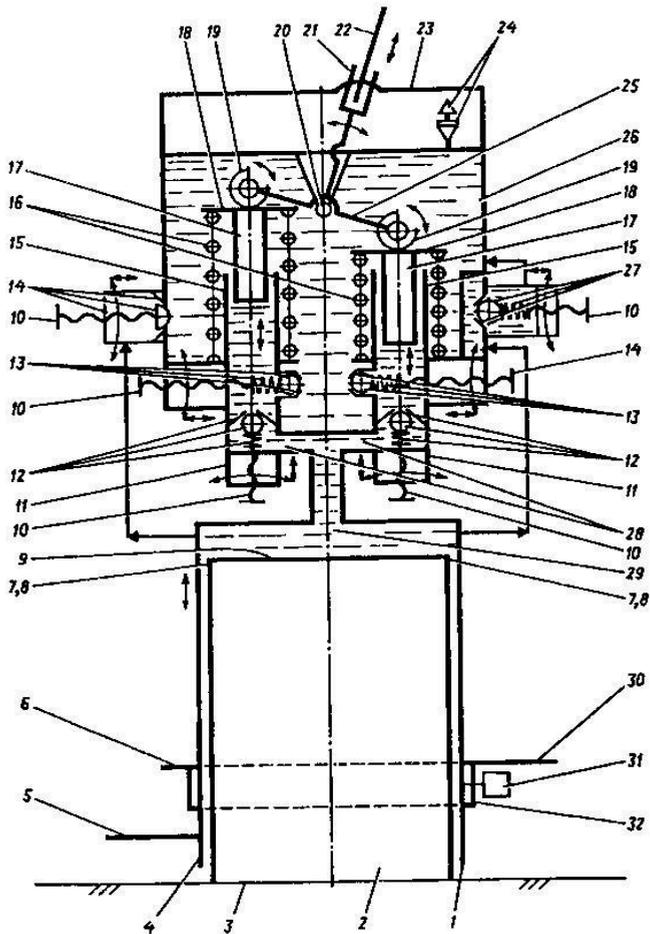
Структурная схема домкрата ПДР-8: 1 – подвижный стальной цилиндр; 2 – неподвижный полый поршень; 3 – опорная плита; 4 – направляющая втулка; 5 – грузоподъемная лапа; 6 – скоба; 7 – манжета; 8 – уплотнительное кольцо; 9 – шайба; 10 – винтовые заглушки; 11 – панель с каналами; 12 – нагнетающий клапан; 13 – всасывающий клапан; 14 – клапан с запорной иглой; 15 – плунжерная втулка; 16 – пружины; 17 – плунжер; 18 – тарелки; 19 – ролики; 20 – вал; 21 – втулка; 22 – рукоять; 23 – ручка для переноски; 24 – пробка-сапун; 25 – двуплечее коромысло; 26 – масляный резервуар; 27 – предохранительный клапан; 28 – каналы для рабочей жидкости; 29 – гидросистема домкрата; 30 – рихтовочная лапа; 31 – стопорный винт; 32 – передвигной хомут
